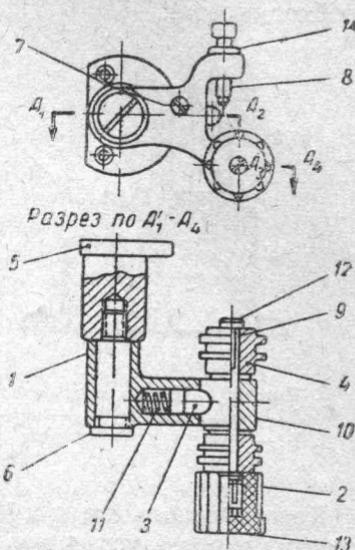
Каретка барабана мальтийского креста: 1 — кронштейн с осью; 2 — головка; 3 — фиксатор; 4 — ролик; 5 — фланец; 6, 7 и 8 — винты; 9, 10 — шайбы; 11 — пружина; 12, 13 — винты; 14 — гайка
